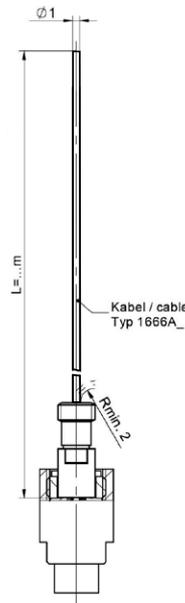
Drucksensor Typ 6172B mit Single-Wire Kabel
